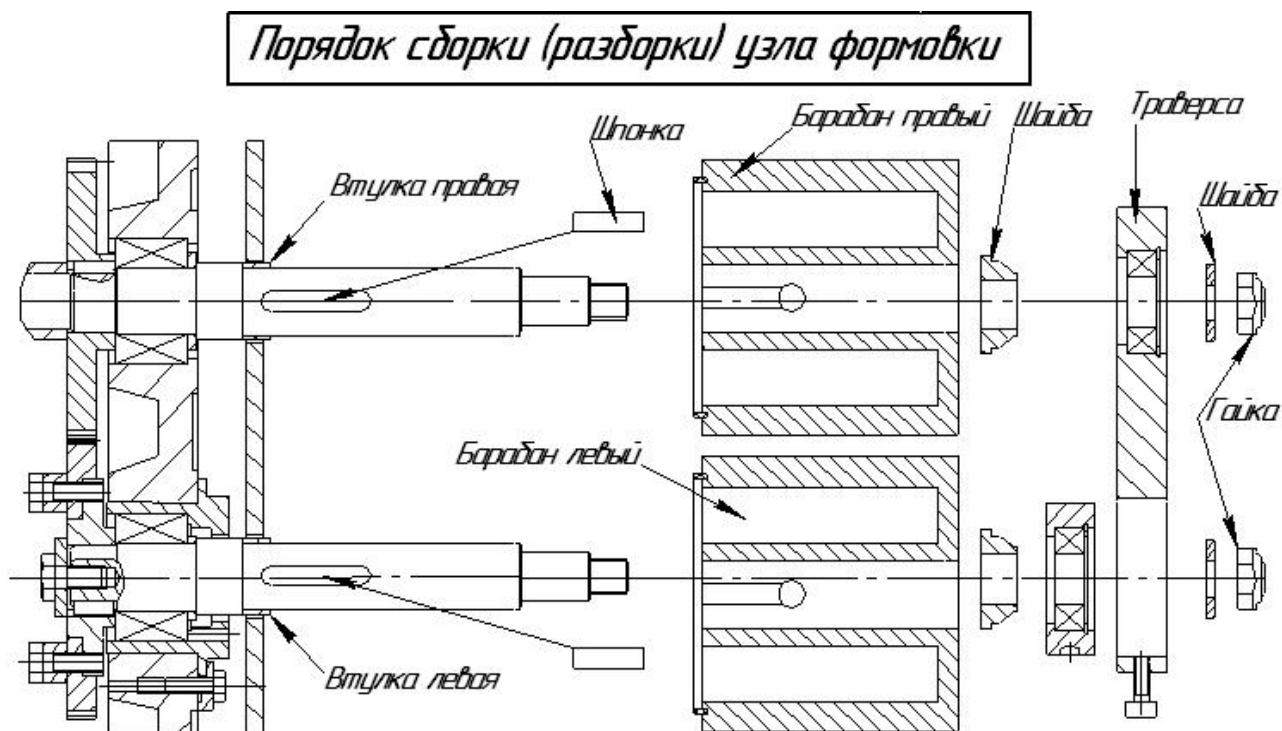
Чертеж - порядок сборки (разборки) узла формовки.
